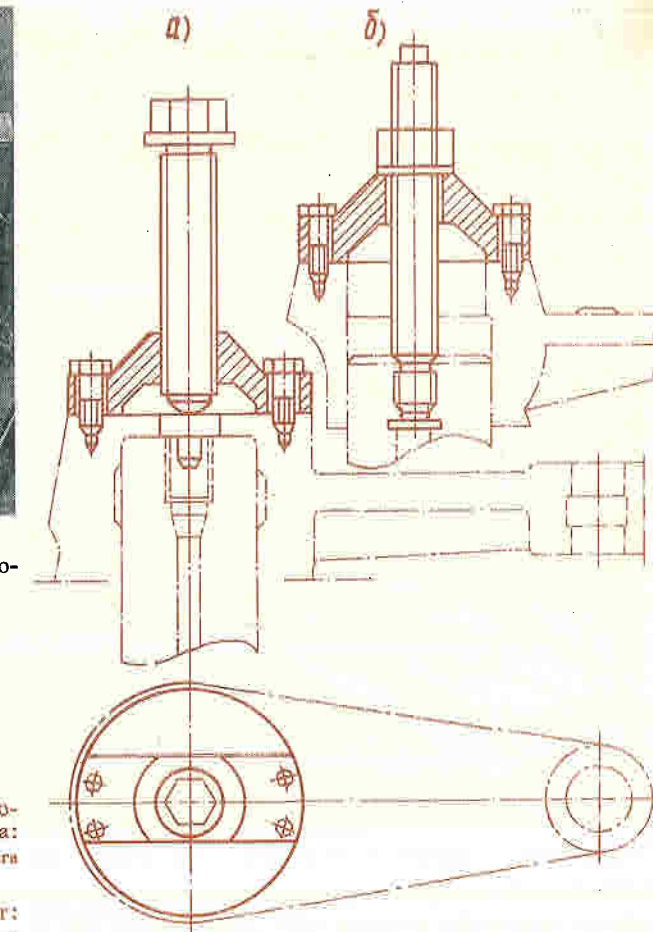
Приспособление для насадки и съема рычагов направляющего аппарата:
